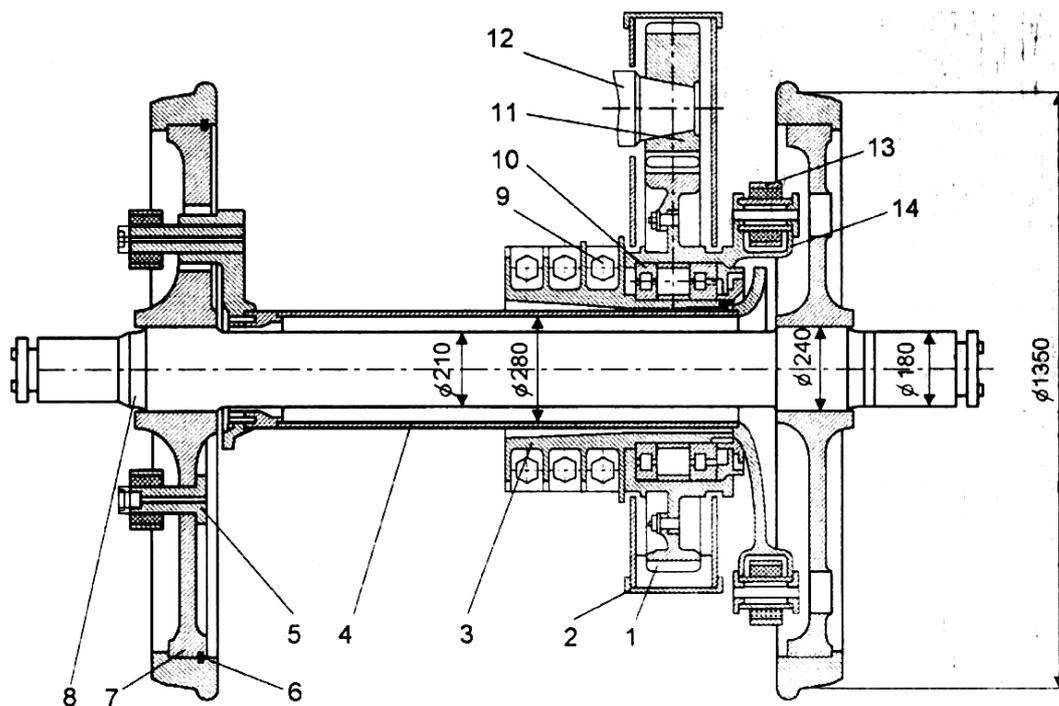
Колесная пара электровоза ВЛ84: 1 - зубчатый венец; 2 - кожух; 3 - невращающаяся цапфа; 4 - полый вал; 5 - палец привода колесного центра; 6 - бандажное кольцо; 7 - колесный центр; 8 - ось колесной пары; 9 - болт крепления цапфы; 10 - роликовый подшипник зубчатого колеса; 11 - шестерня; 12 - вал тягового двигателя; 13 - шатун с резинометаллическими втулками; 14 - центр зубчатого колеса
